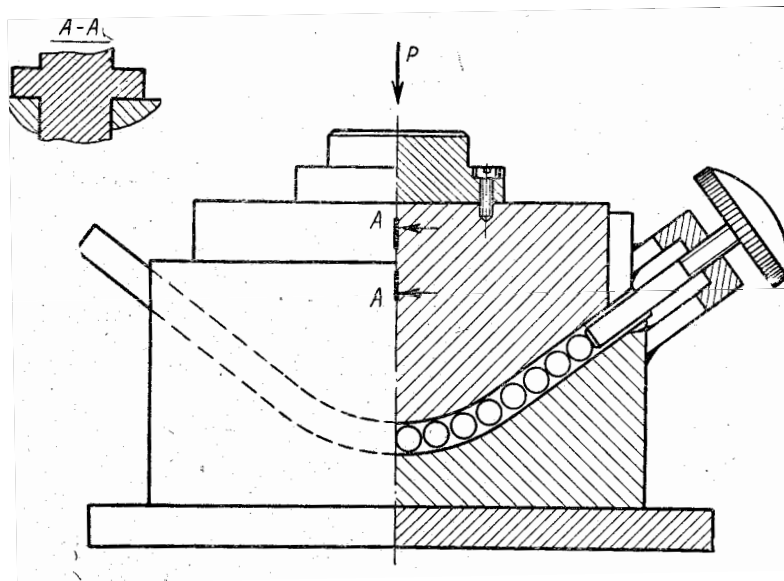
Винтовое приспособление для калибровки изогнутых труб
